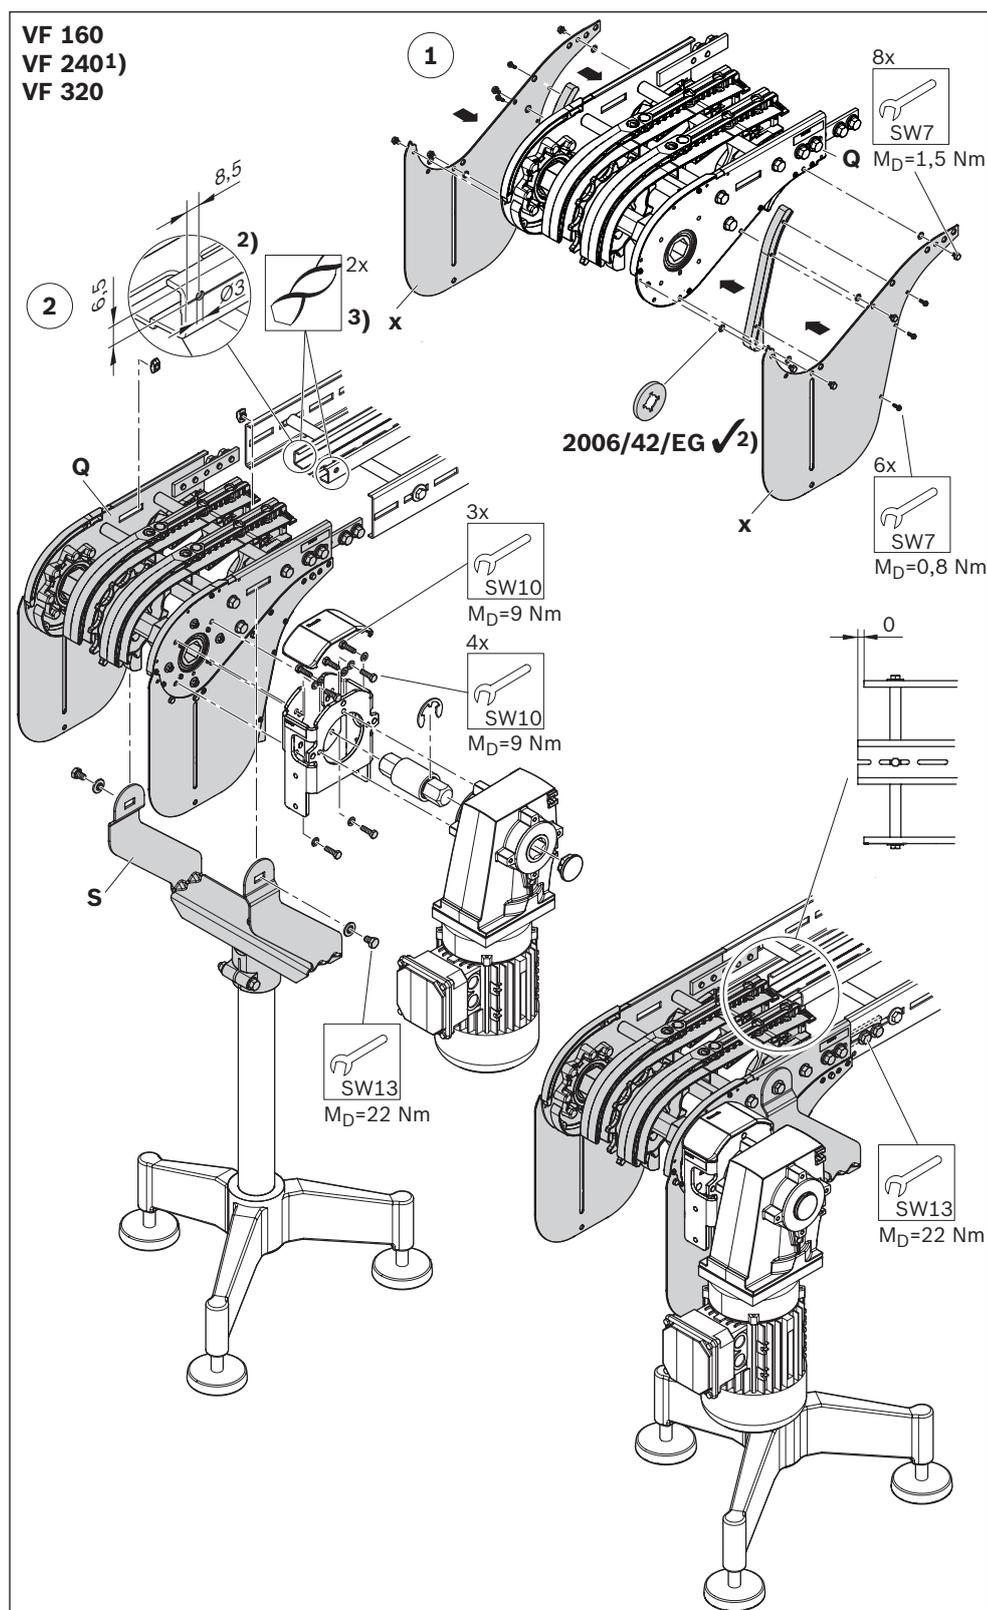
Sistema STS, montaje de la unidad básica, VF 160/VF 240/VF 320
